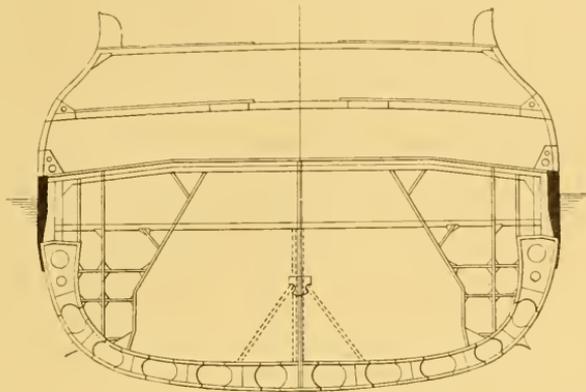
Coupe transversale d'un vaisseau de ligne de construction ancienne.
